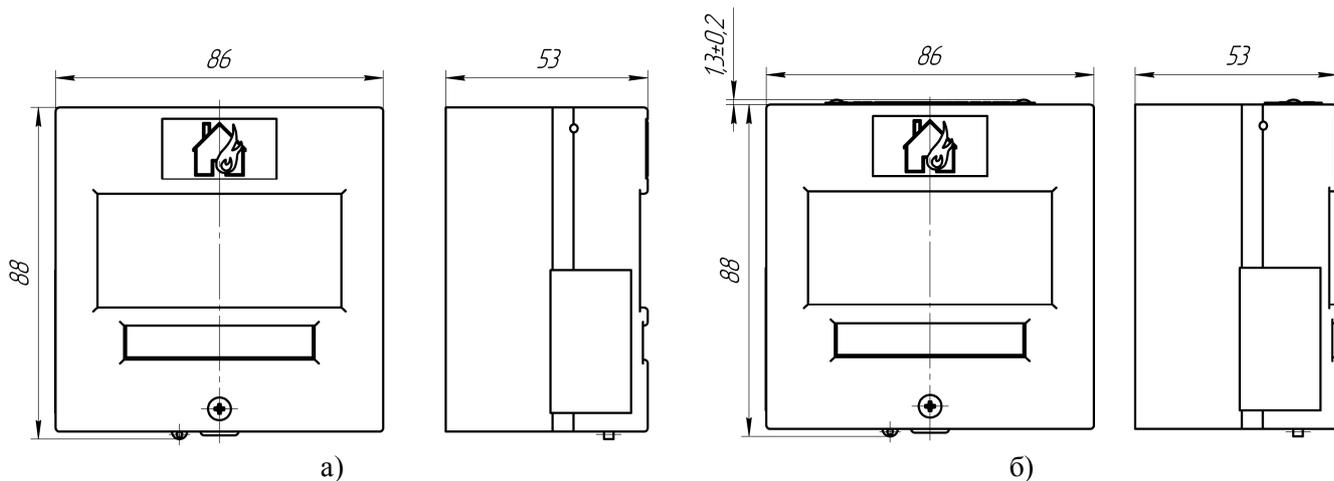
Внешний вид и габаритные размеры извещателей ИПРА (а) и ИПРА-В (б), размеры в мм
